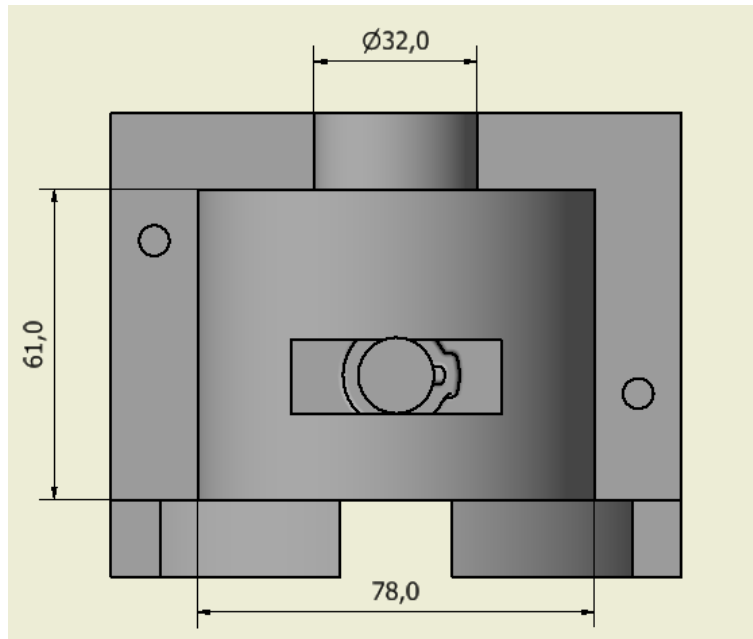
Vista en frontal del sistema de fundición del aluminio.
